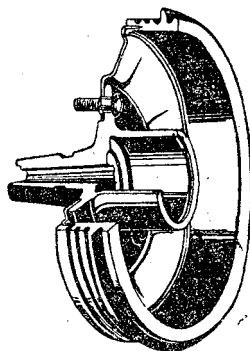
Тормозной барабан и ступица заднего колеса в сборе.
